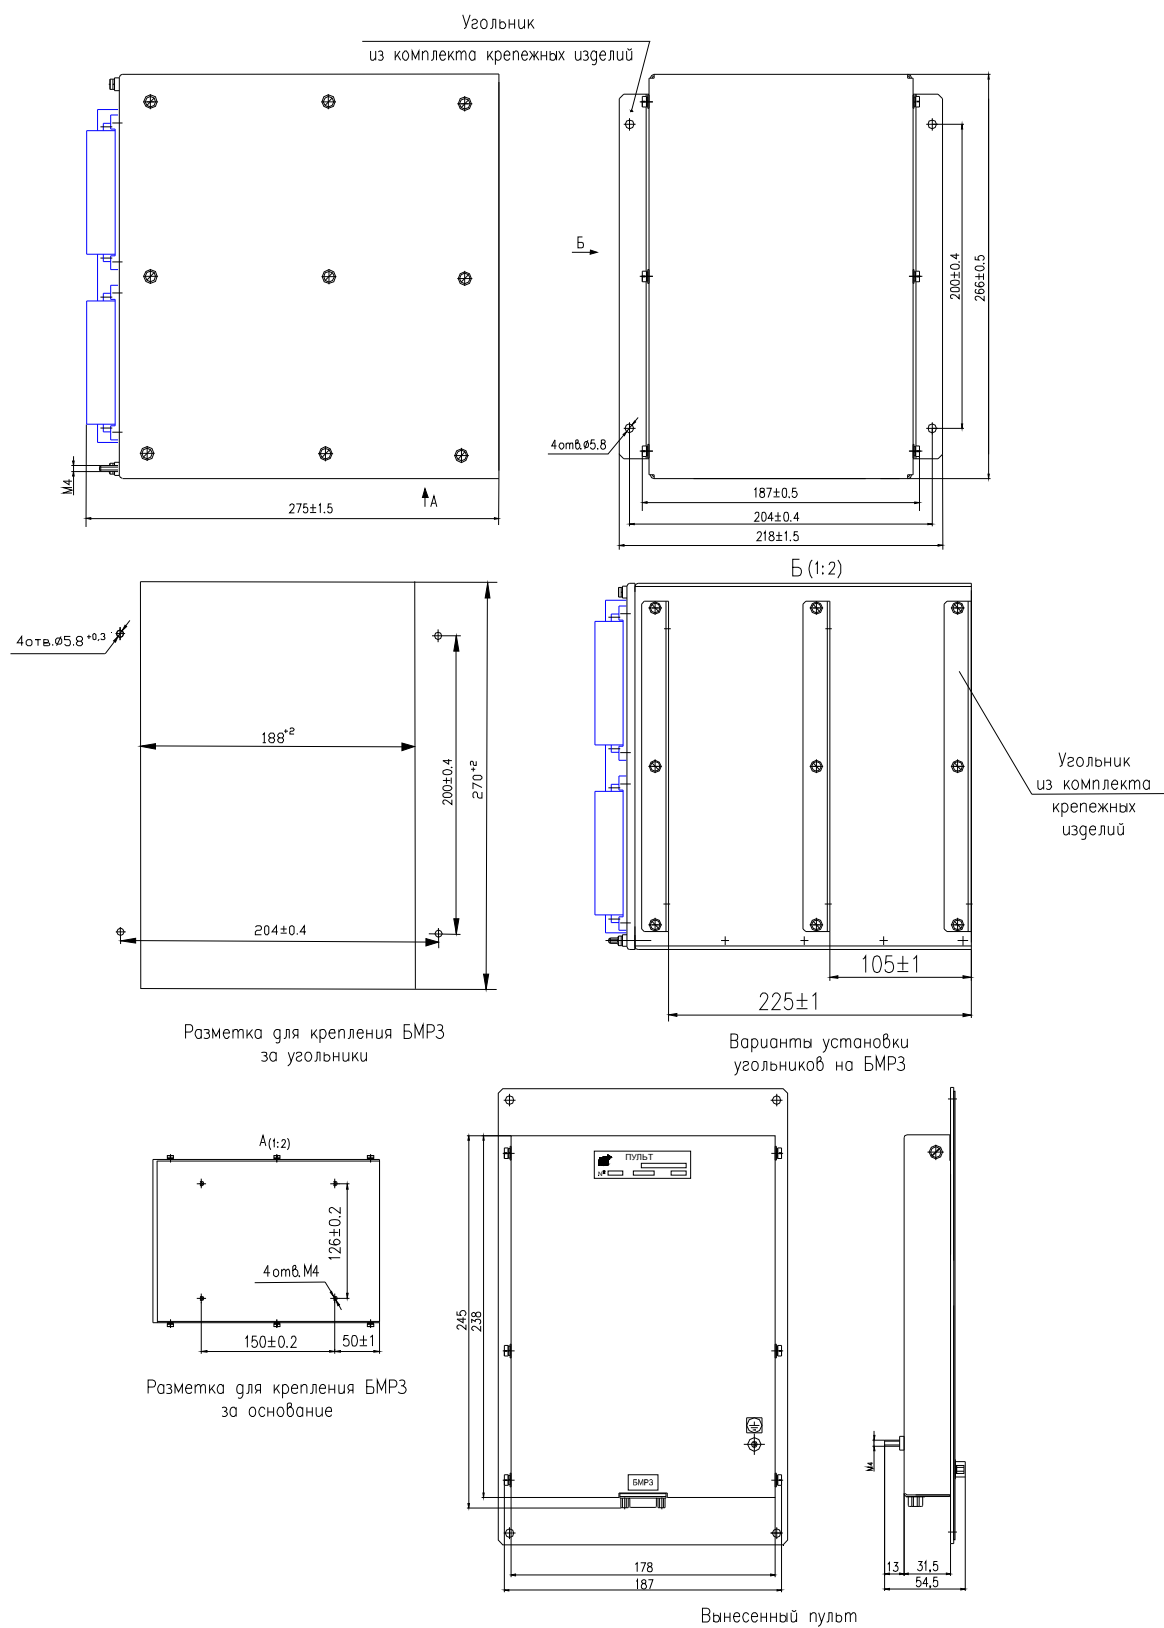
(лист 3 из 3) в - Габаритные, присоединительные и установочные размеры для БМР3 ДИВГ.648228.071
